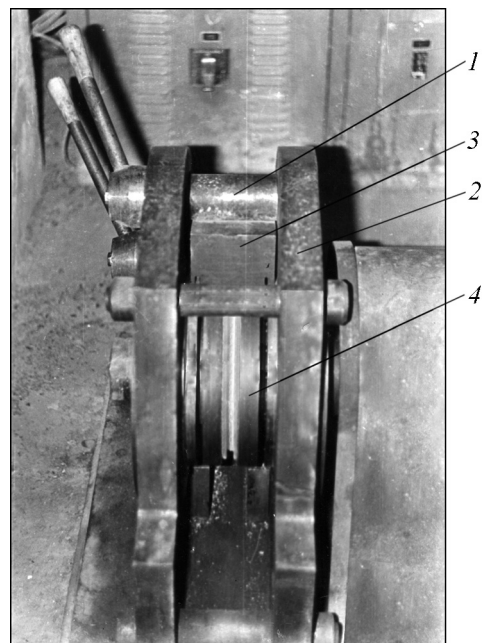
Прессовый узел лабораторной установки «Конформ»
